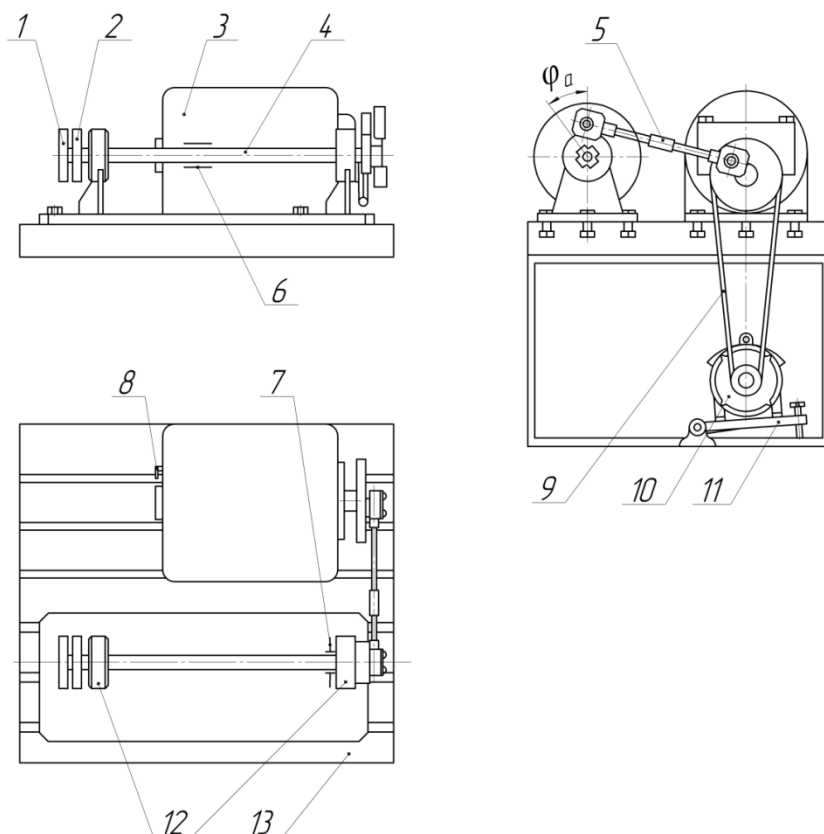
Схема установки для проверки гасителей крутильных колебаний:
